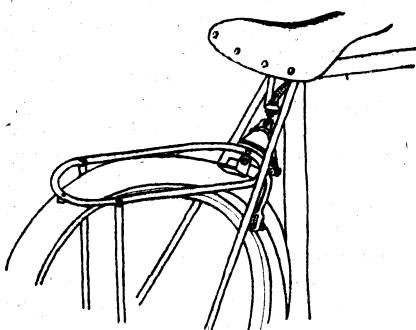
Крепление багажника из дюралюминиевых трубок.
